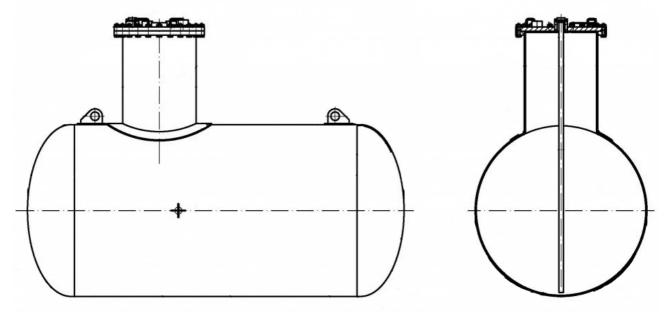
Общий вид эскиза резервуара РГС-50
